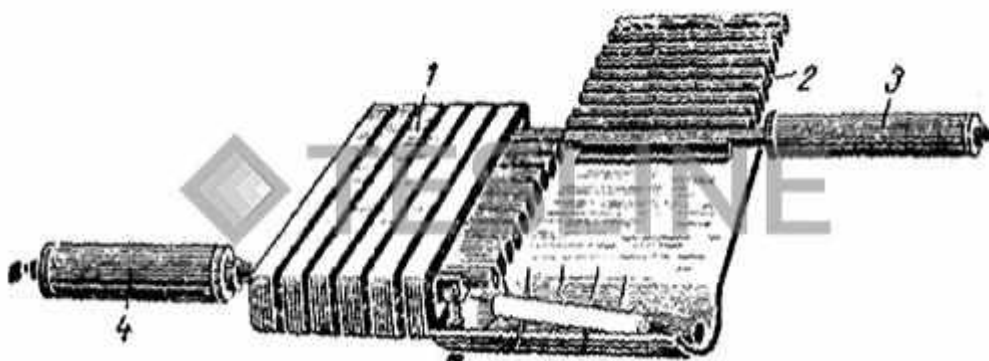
Схема нагревателя для нагрева концов заготовок, длина которых в несколько раз больше их диаметра:
